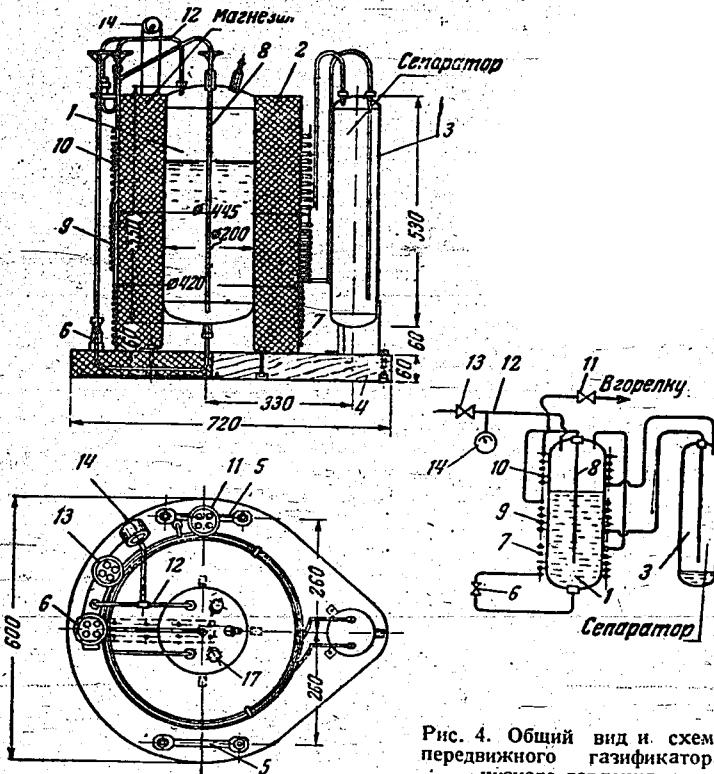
Общий вид и схема передвижного газификатора низкого давления.
